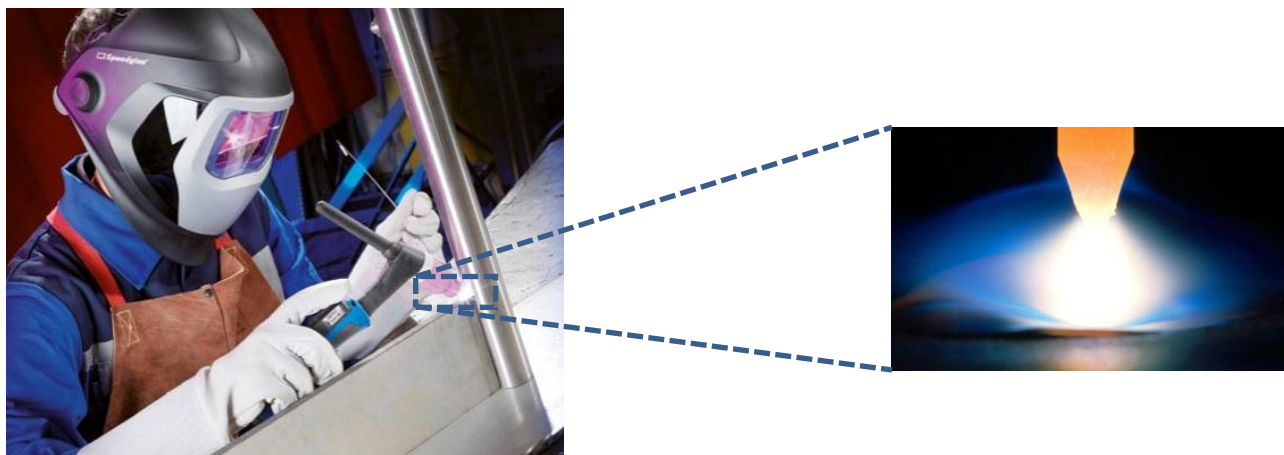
Soldador executando uma soldagem e detalhe do arco elétrico (Binzel, 2016).
